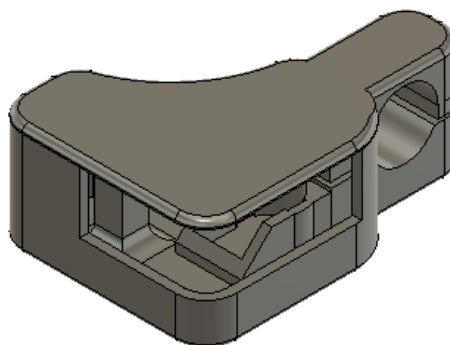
Projeto em CAD do Suporte Superior do Manicoto.
